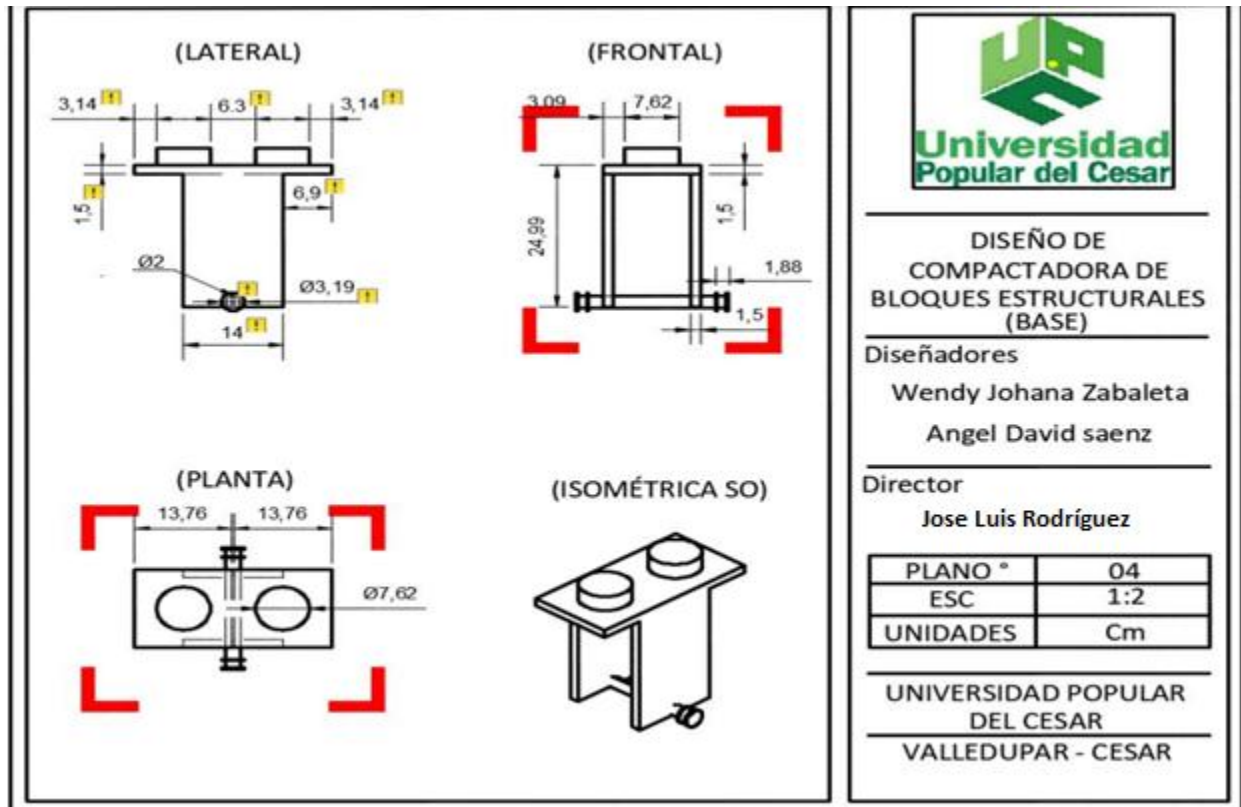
Vista lateral, en planta e isométrica de la base de la máquina.
